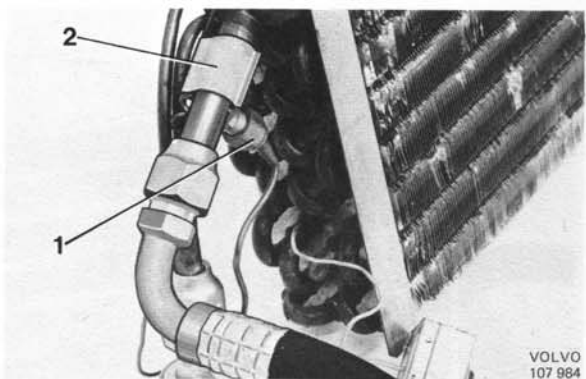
Ausbau des thermischen Expansionsventils, spät. Ausf.
